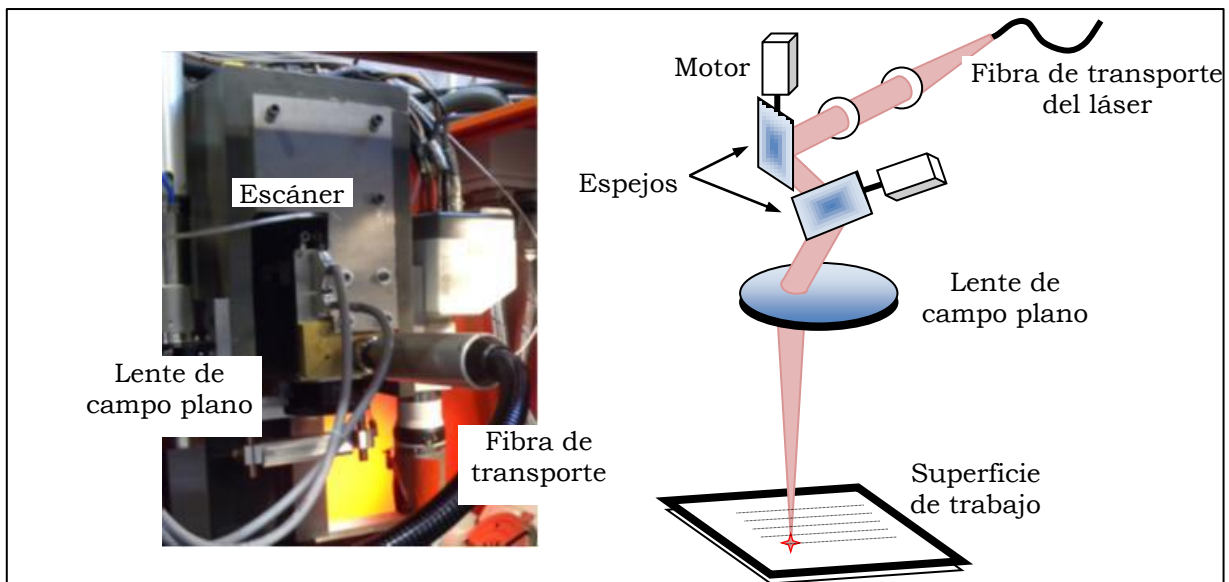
Escáner utilizado para la parte experimental (Izq.) y esquema de los componentes de un escáner (Dcha.).
